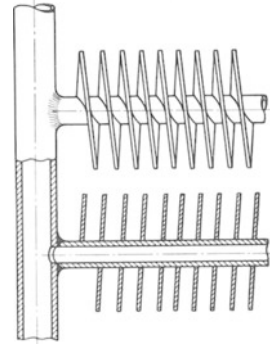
Schweißung von Spiralrippenrohren.
